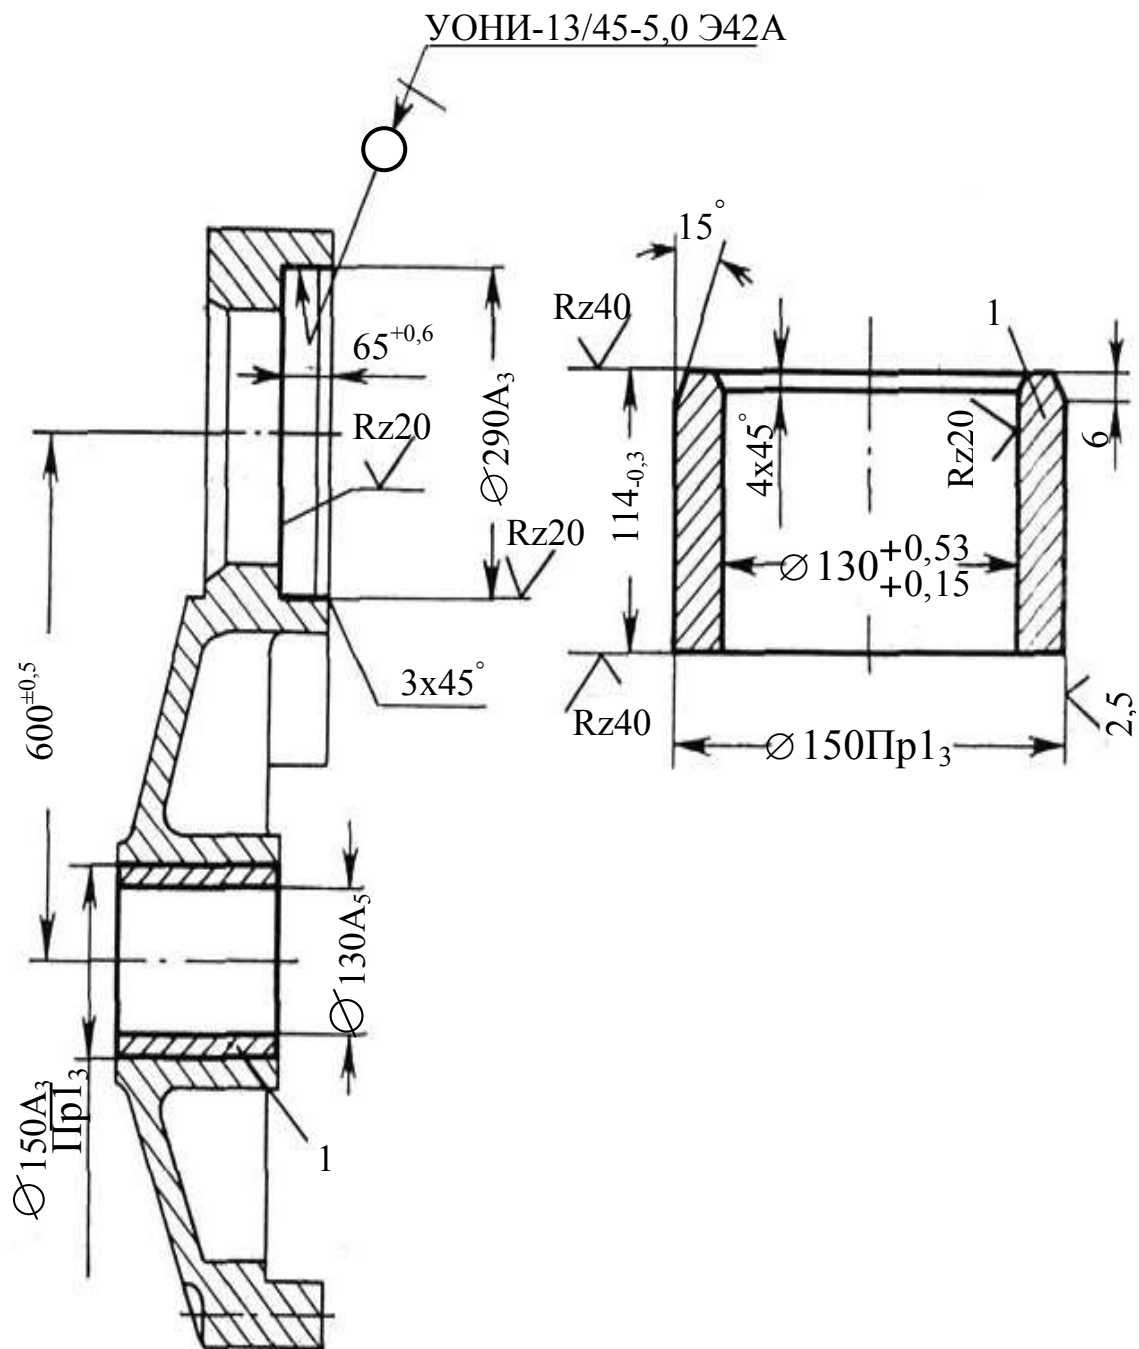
Ремонтный чертеж половины обоймы блока верхней подвески ковша: 1 – *ремонтная втулка
